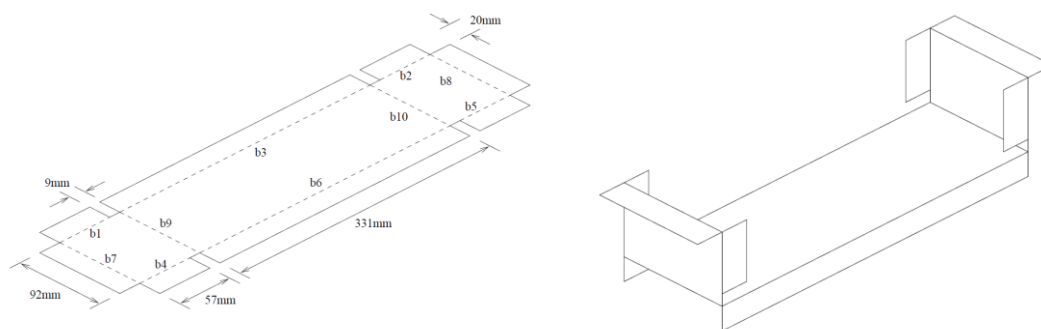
Chapa com linhas e sequência de quinagem (à esquerda) e quinagem completa (à direita)
